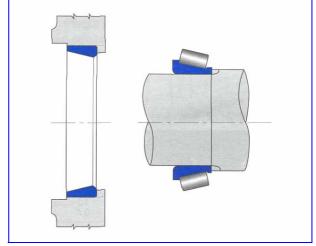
Пазы или канавки под съемник, облегчающие демонтаж подшипника.
